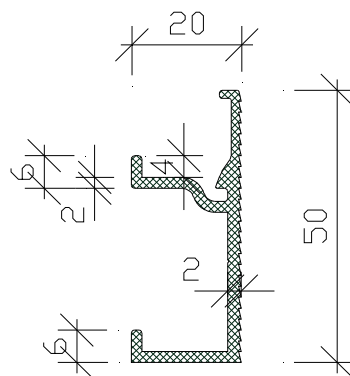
is – Pièce d'aboutage des rails horizontaux 06'75
